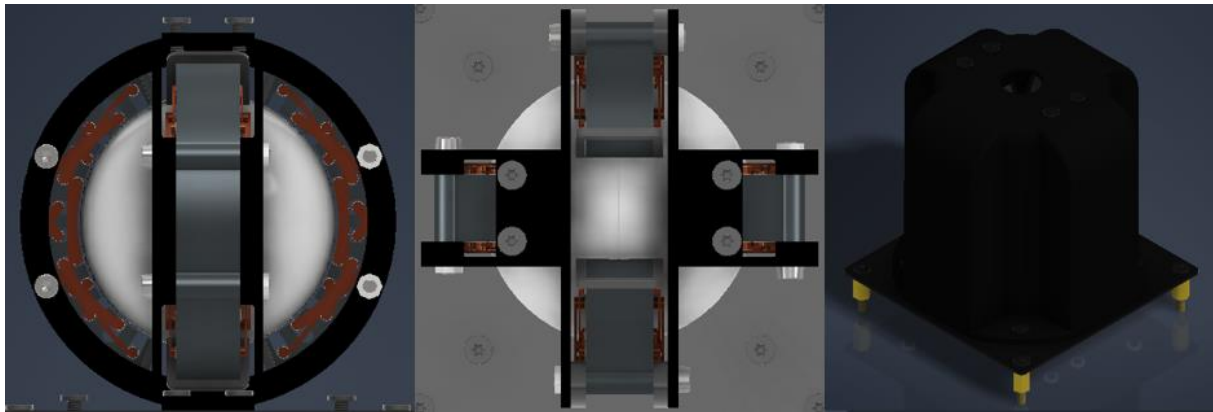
Montagem mecânica dos conjuntos de rotor, bloco de estator e suas bobinas, fixação dos parafusos, carcaça do motor e representação da placa de circuito.
